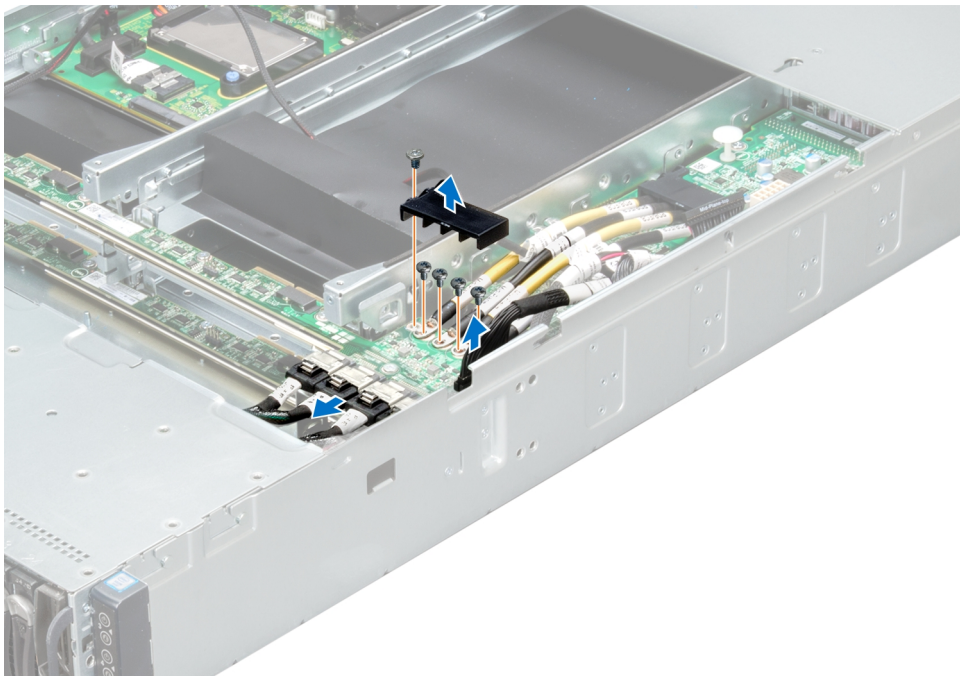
Extracción de los cables de alimentación y la cubierta
